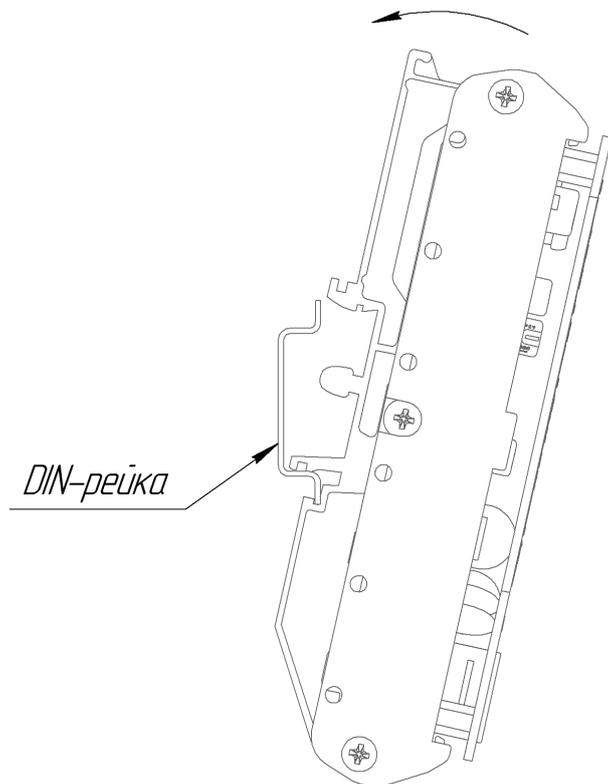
Установка DIN-рейки в паз сетевого коммутатора
